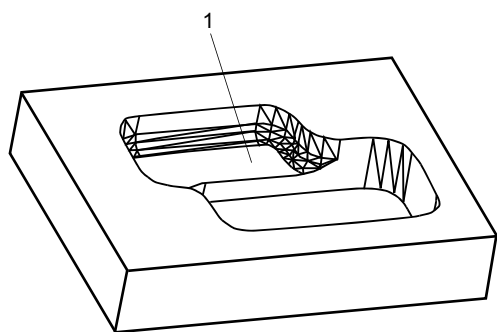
Конструктивный элемент 1 заготовки, получаемый фрезерованием
